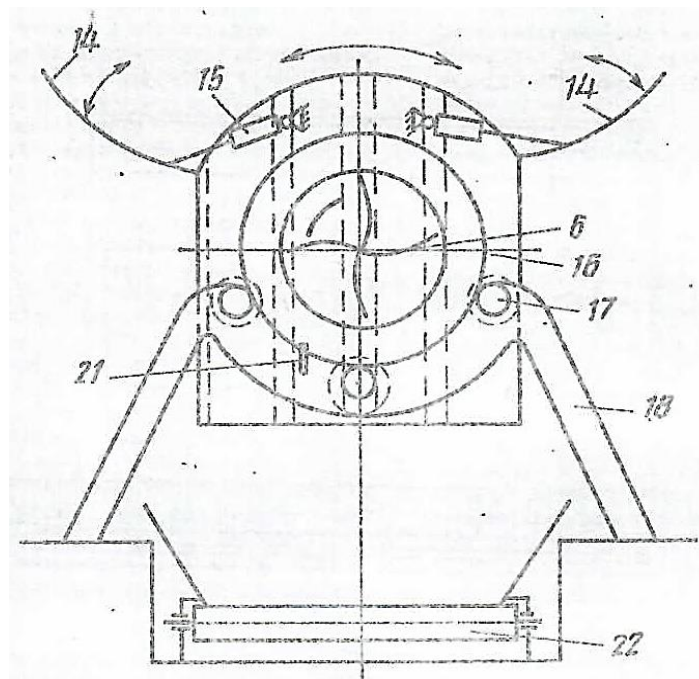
Пристрій для сушки [9], вид збоку
